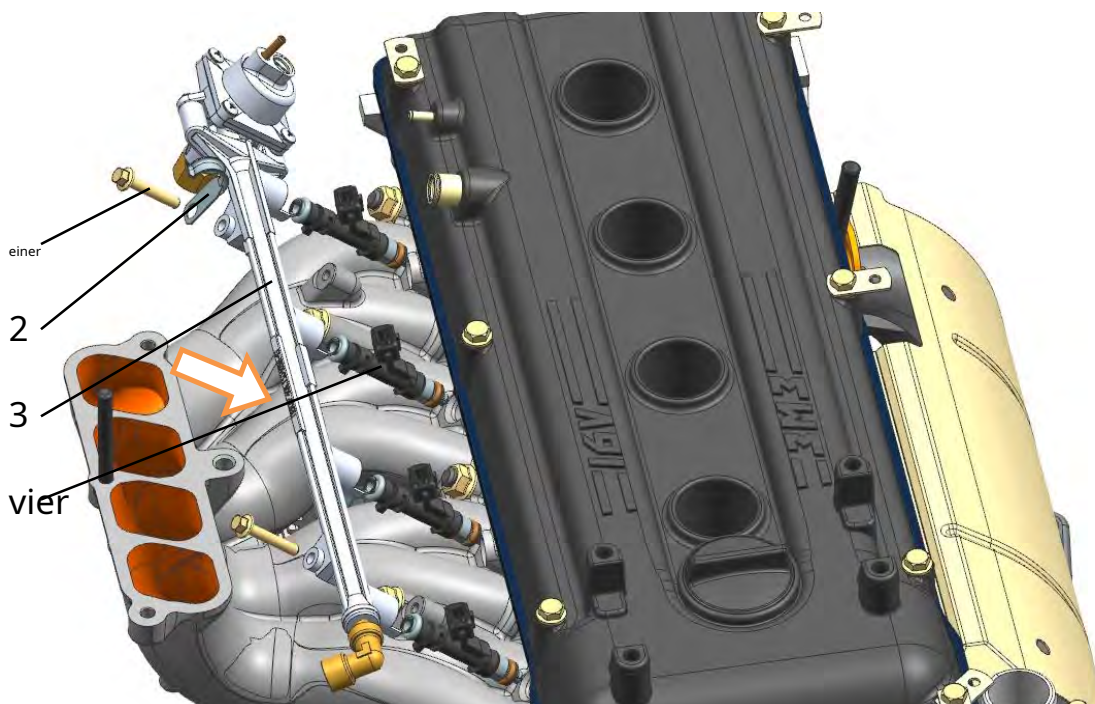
Einbau einer Kraftstoffleitung mit Injektoren:
